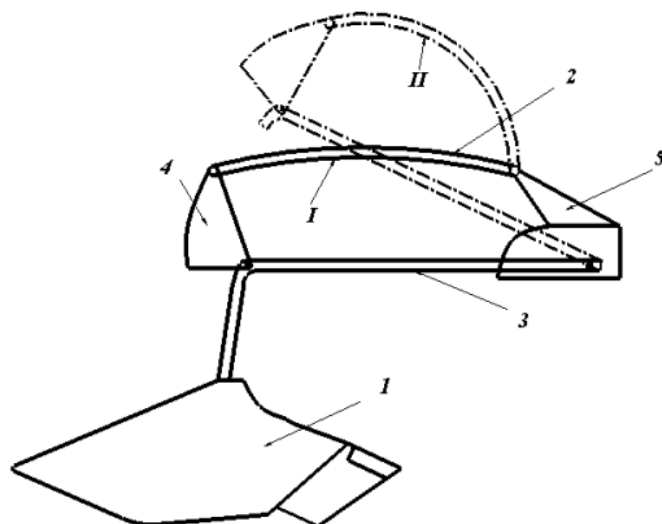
Схема работы защитного механизма корпуса плуга: I – положение рессорной защиты при вспашке; II – положение срабатывания упругого элемента при наезде на препятствие; 1 – Корпус плуга; 2 – Упругий элемент; 3 – Грядиль; 4 – Кронштейн подвижный; 5 – Кронштейн неподвижный
